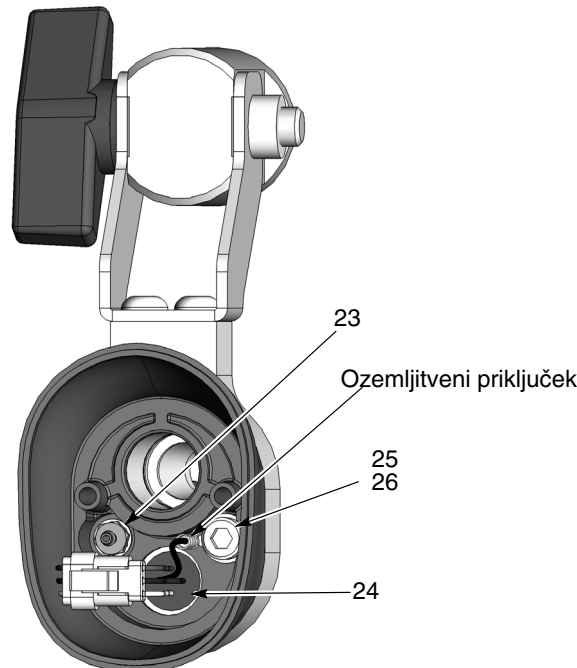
Razstavljanje pištole – Zamenjava cevi za prah
